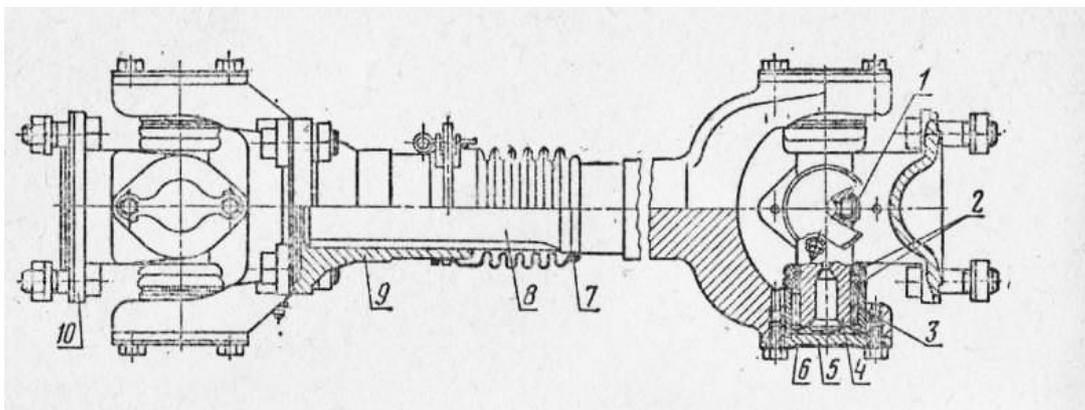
Карданная передача к переднему мосту трактора Т-150К: 1 — клапан; 2 — сальники; 3 — иголки подшипника; 4 — крестовина; 5 — опорная пластина игольчатого подшипника; 6 — стопорная пластина; 7 — чехол шлицевого соединения; 8 — шлицевой вал вилки переднего кардана; 9 — шлицевая муфта; 10 — присоединительный фланец
